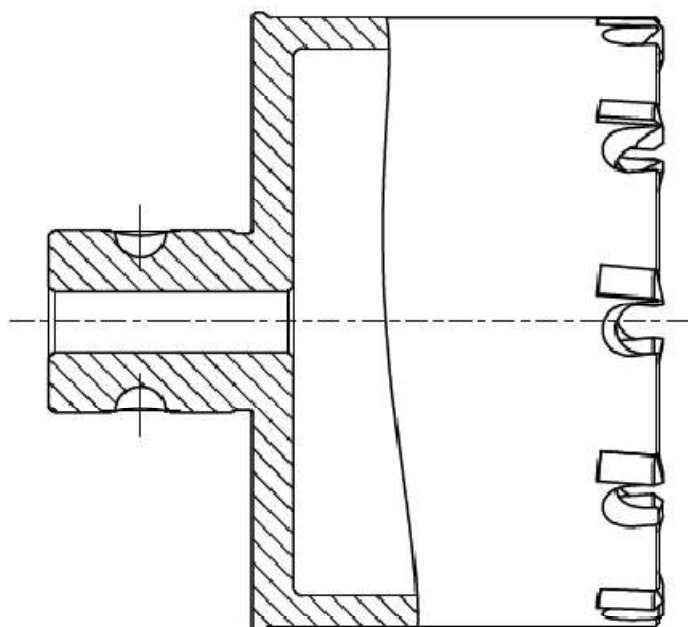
Корончатє свердло з твердосплавними напайними пластинами фірми Fein
